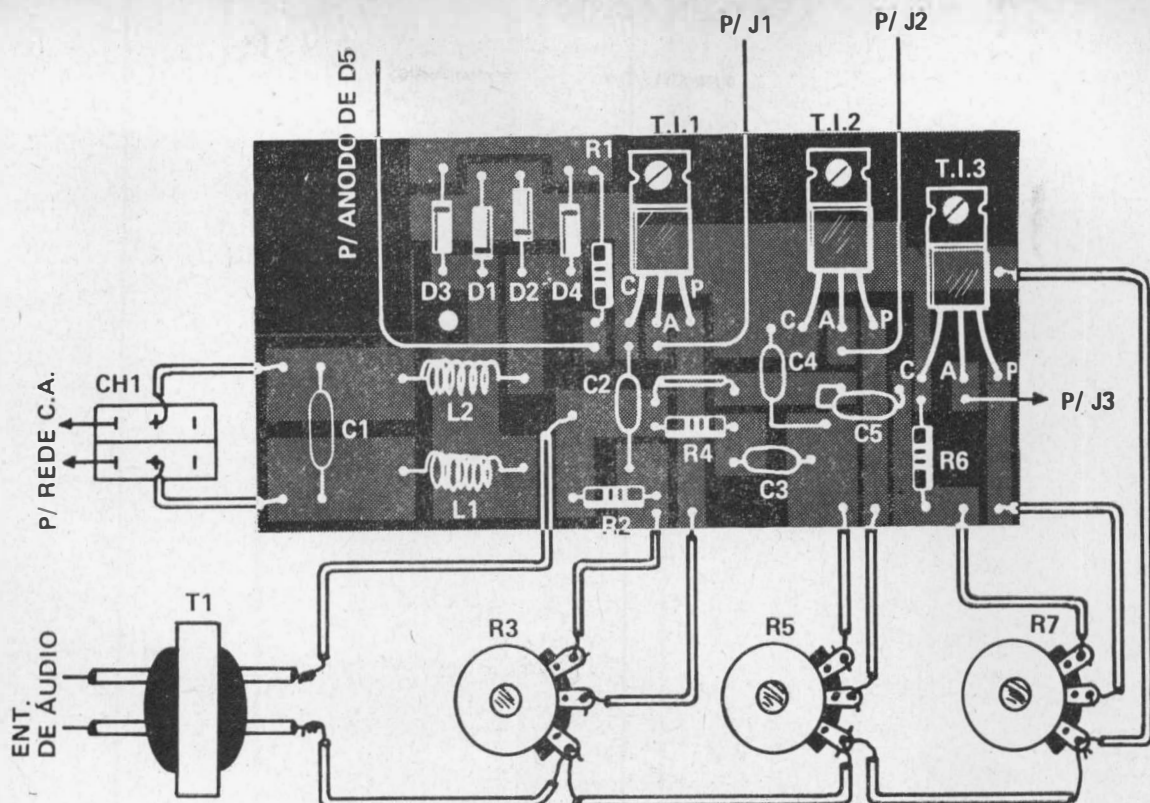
Disposição dos componentes sobre a plaqueta da Fig. 2.
